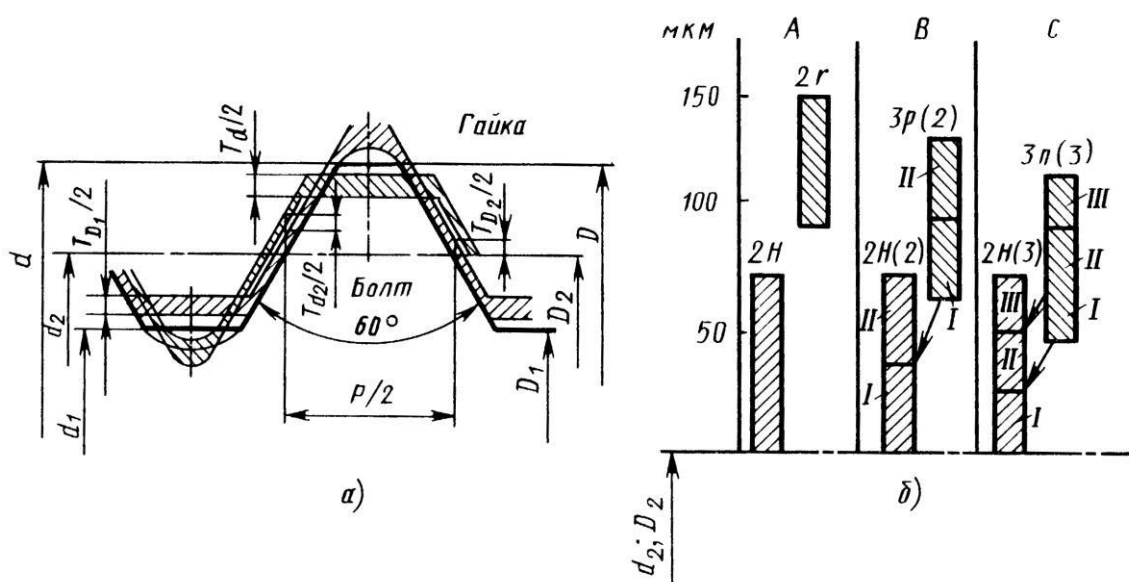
Схемы расположения полей допусков диаметров (а) и среднего диаметра (б) резьбы с натягом
